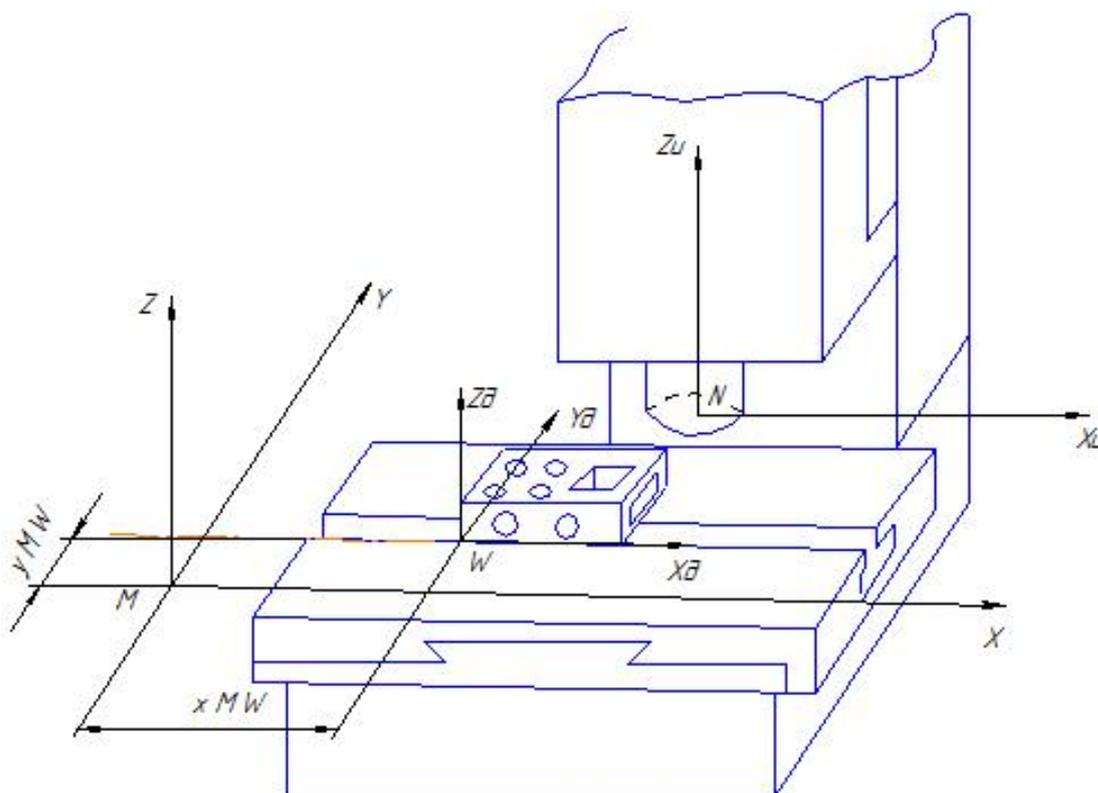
Системы координат фрезерного станка с ЧПУ
